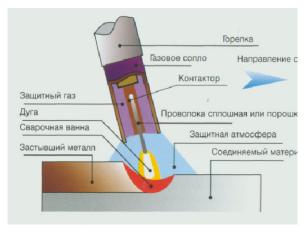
Технология сварки в защитном газе
